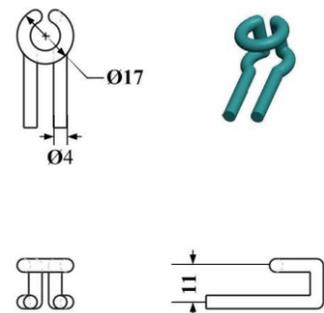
射出產品之 3D CAD 模型與幾何尺寸
